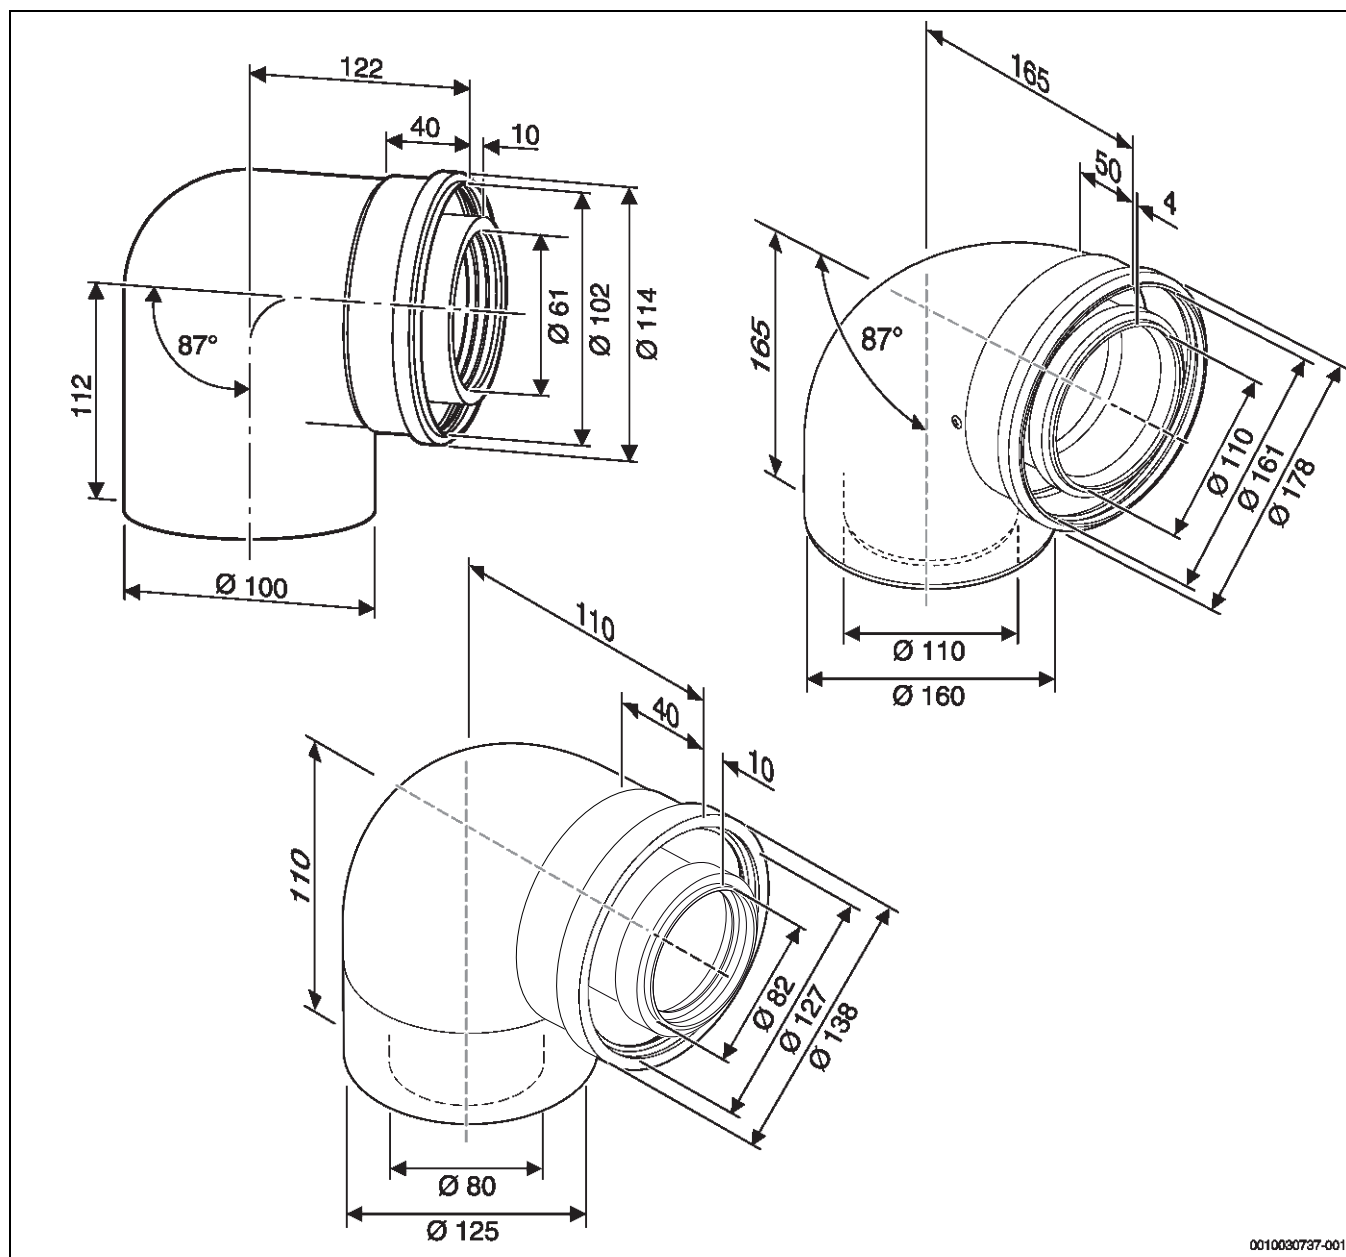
Bogen mit Prüföffnung, 87°, Ø 80 mm
